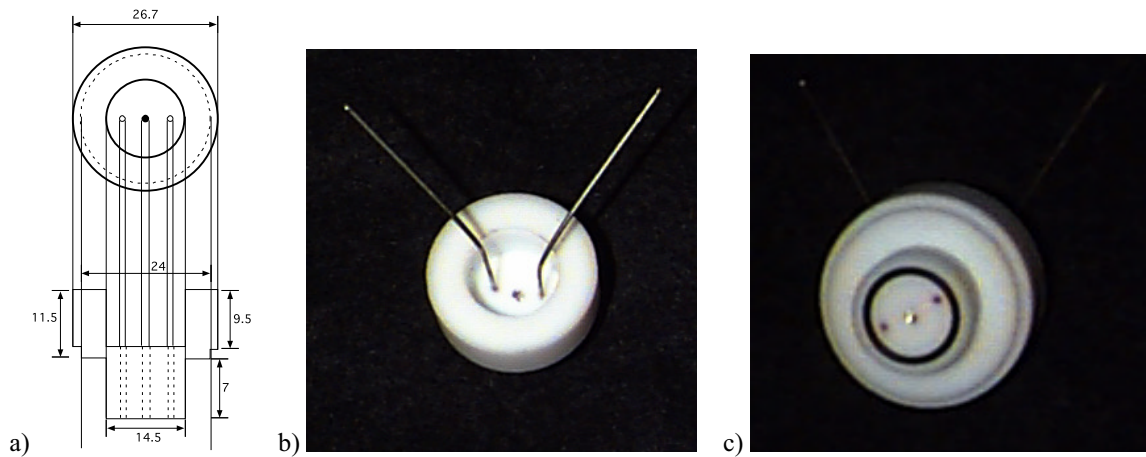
a) Konstruktionszeichnung für den neuen Tauchkolben b) Foto von oben. Zu sehen sind Ein- und Auslas für das Zellmedium und die Referenzelektrode aus Platin in der Mitte. c) Foto von unten. Der schwarze O-Ring dichtet die entstehende Kammer aus Tauchkolben und Chip ab.
